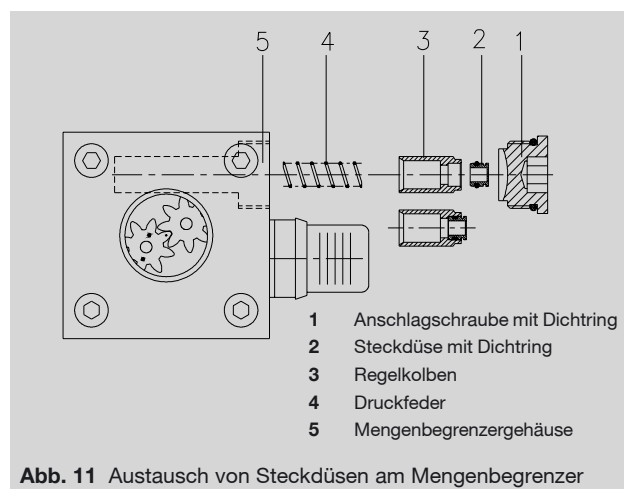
Austausch von Steckdüsen am Mengenbegrenzer
